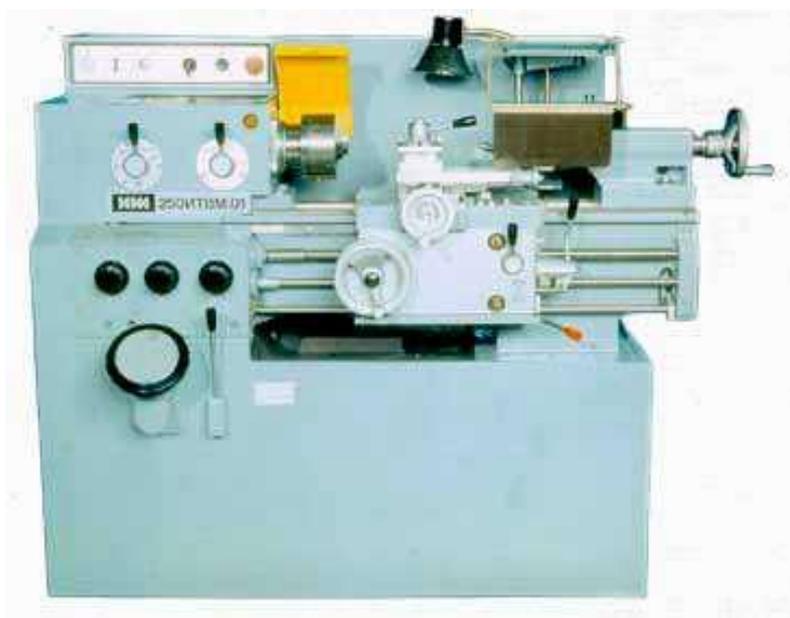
Станок токарно-винторезный модели 250ИТВМ.01
